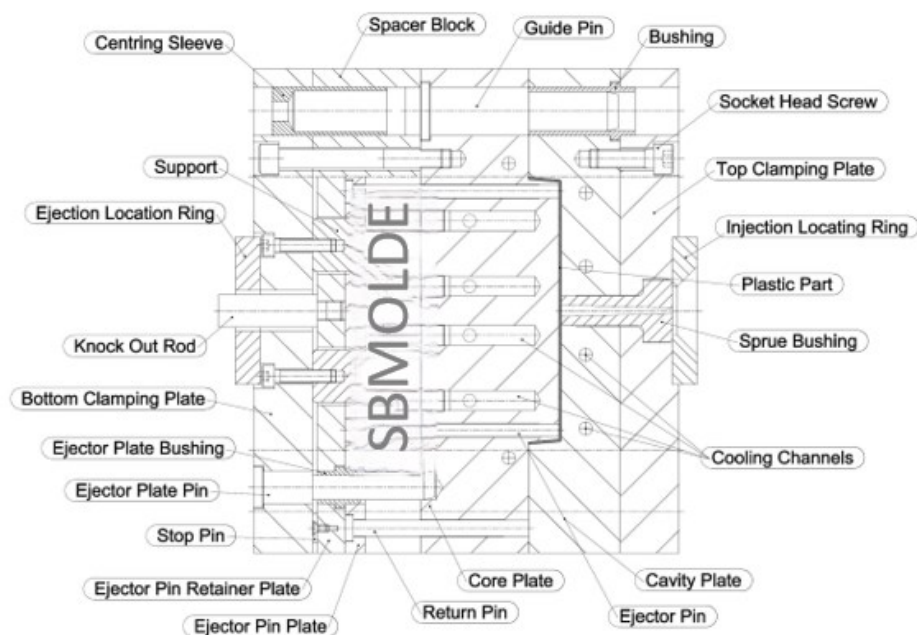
Desenho de um molde, com os vários componentes (Cortesia da Sbmolde Lda).
